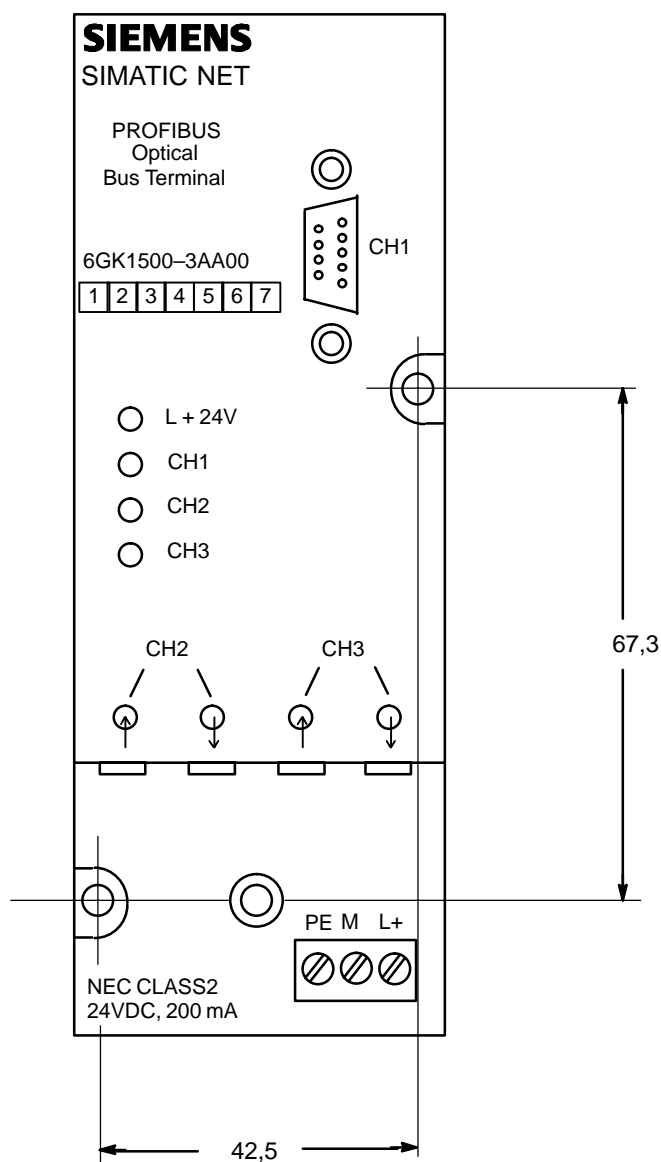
Installazione di un modulo su una piastra di montaggio
